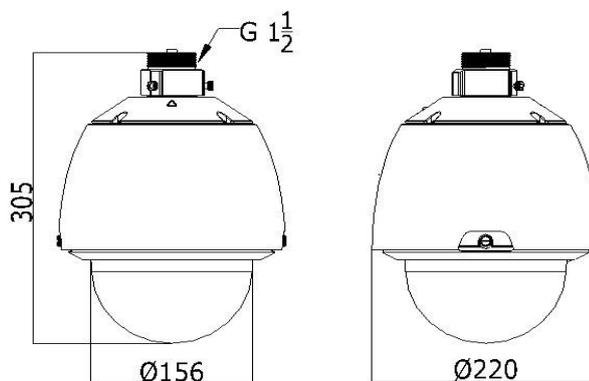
Габаритные размеры IP-видеокамеры SDP-825
